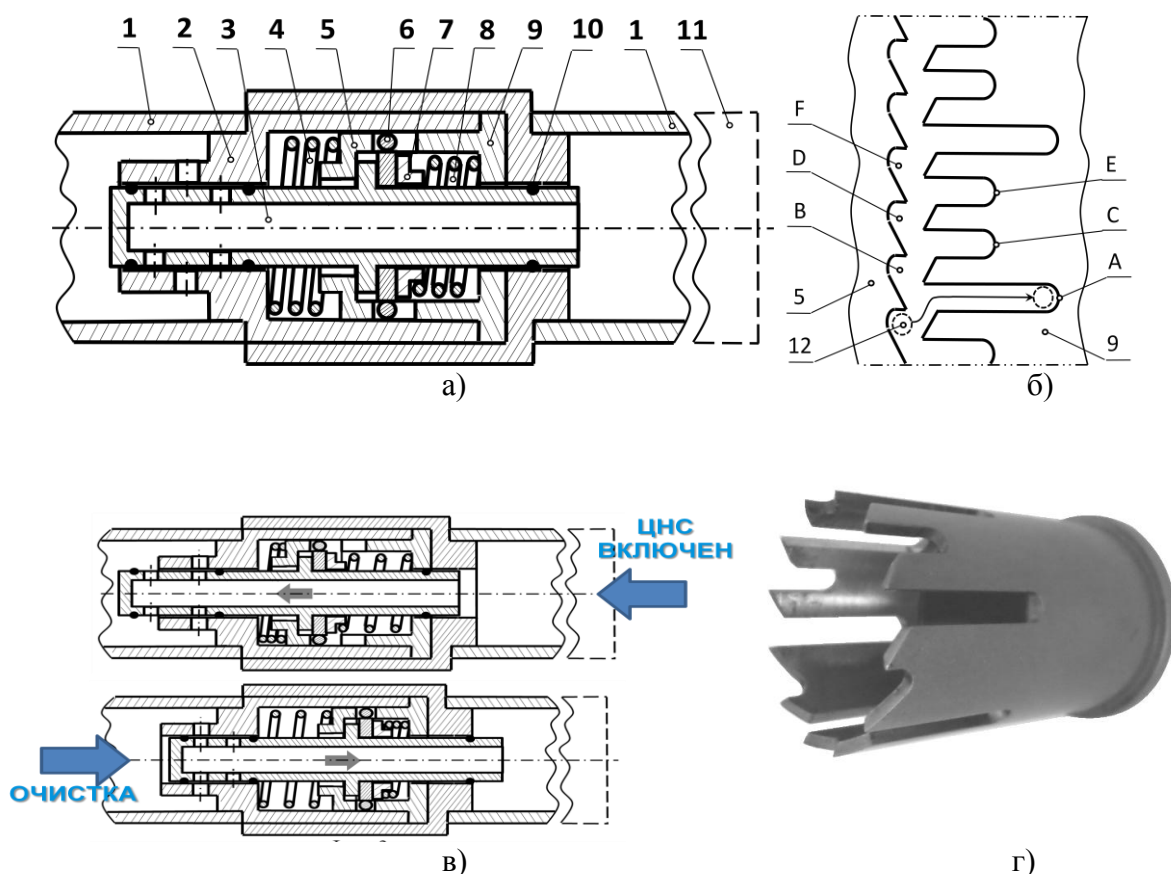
Трехрежимный аналоговый клапан для очистки насосов, насосно-компрессорных труб и фильтров: *а* – общий вид; *б* – развертка седла (поз. 9); *в* – схема работы; *г* – фотография прототипа седла; А – направляющий паз режима очистки; В, D, F – впадины звездочки напротив пазов А, С, Е; С, Е – направляющие пазы режима нейтрального положения; 1 – насосно-компрессорная труба; 2 – корпус с выходными отверстиями; 3 – шток клапана; 4,8 – пружины; 5 – втулка; 6 – сепаратор; 7 – опорная шайба; 9 – седло; 10 – уплотнительные кольца из эластичного материала; 11 – фильтр; 12 – шарики.
